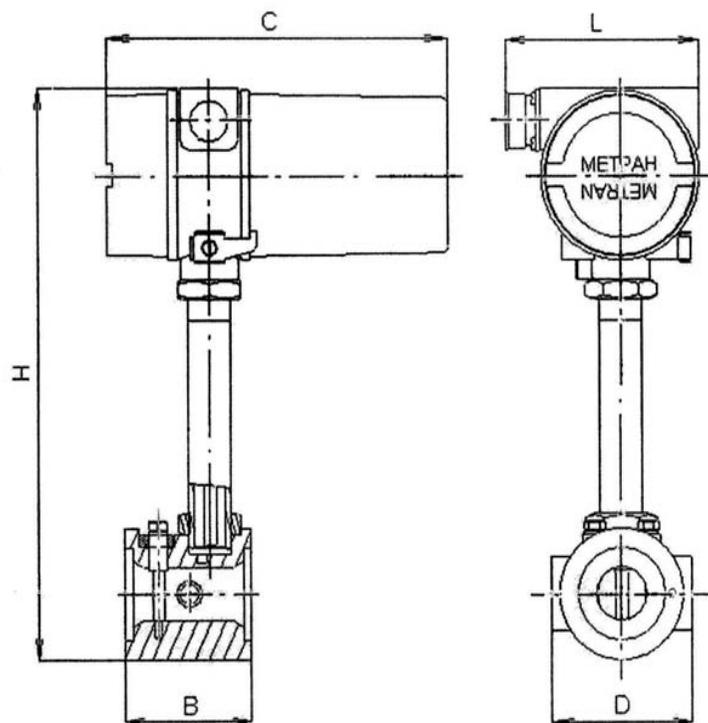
Габаритные и установочные размеры преобразователя исполнения А.
